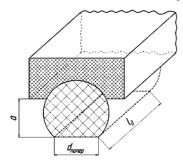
Схема срезания одним зерном объема металла с поверхности обрабатываемой детали
